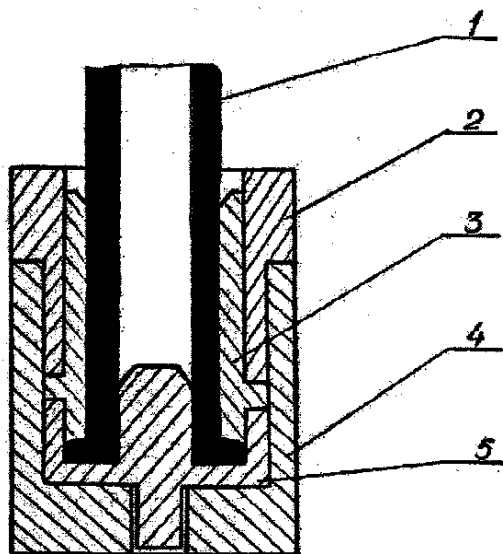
Прессформа для изготовления полиэтиленовых рукавов
